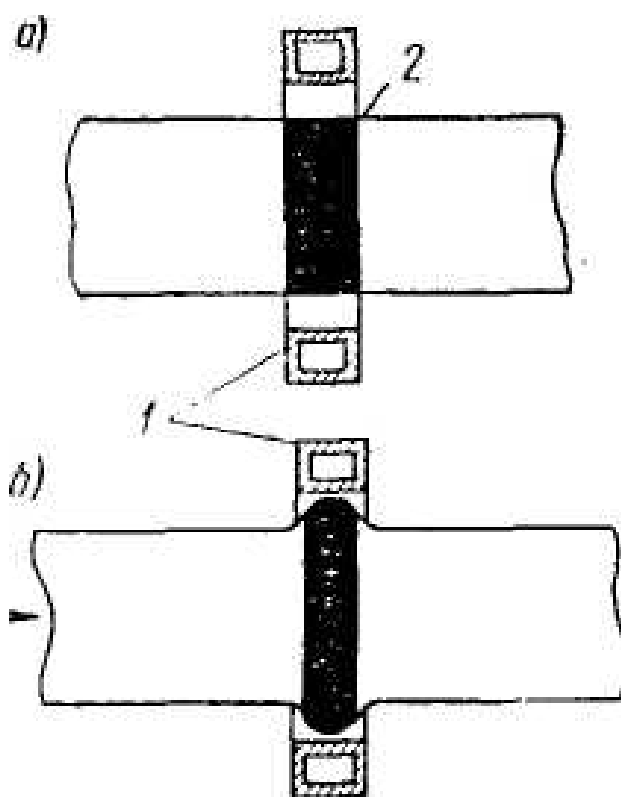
Схема сварки без оплавления: а – нагрев, б – осадка.
